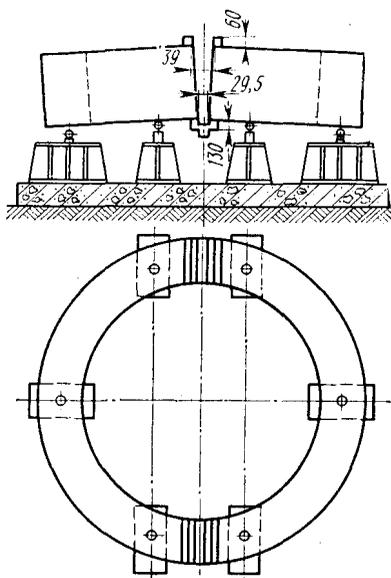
Сборка половин бандажа под сварку
